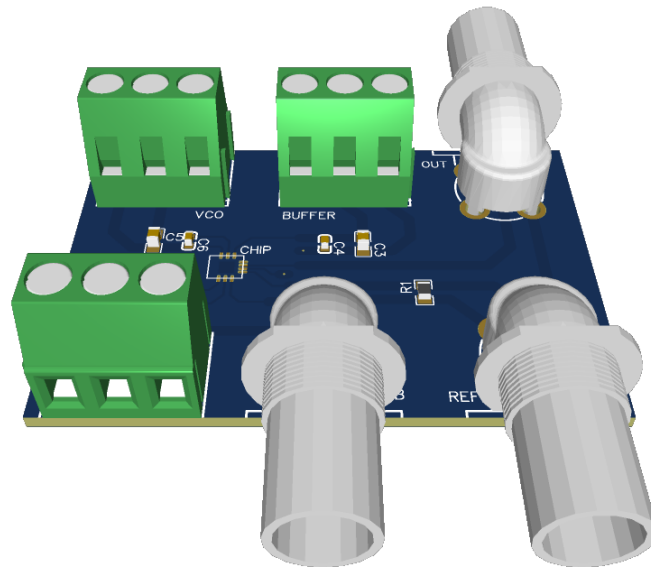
Esboço 3D da placa de teste. Fonte: Autor
